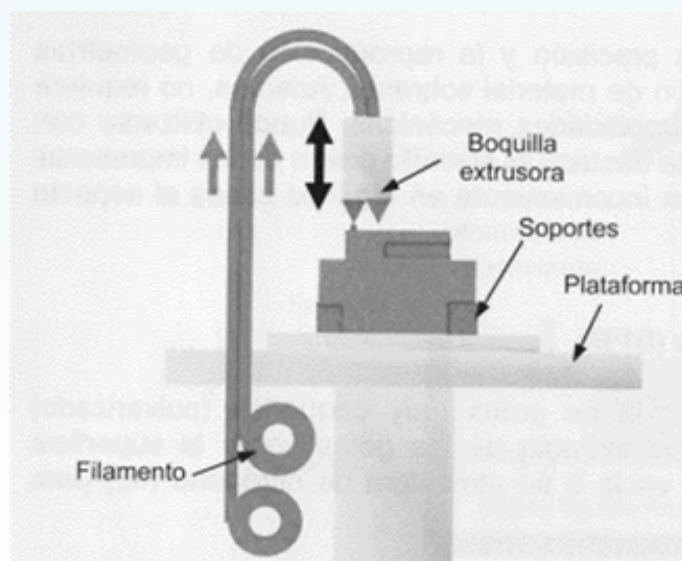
Vista del procedimiento de impresión 3D, método de deposición de fundida FDM, extraído de Gómez S, Impresión 3D. Copyright©
